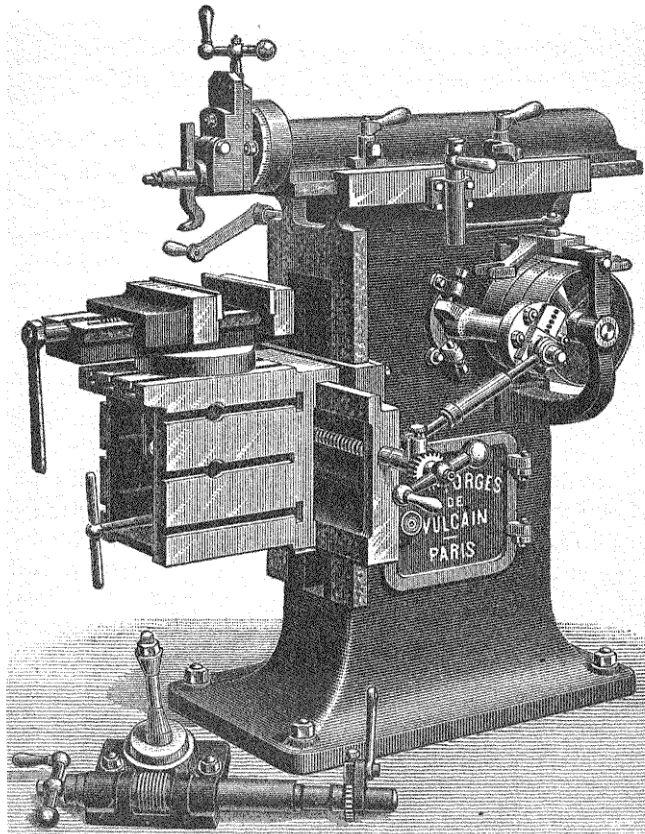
Étau-limeur Chouanard à double engrenage.
